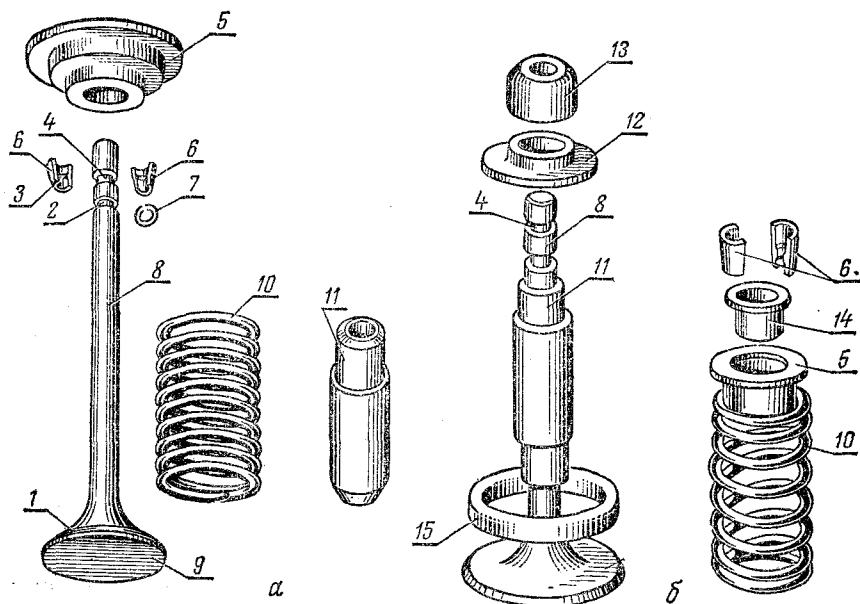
Клапан, пружина и детали ее крепления механизма газораспределения:
